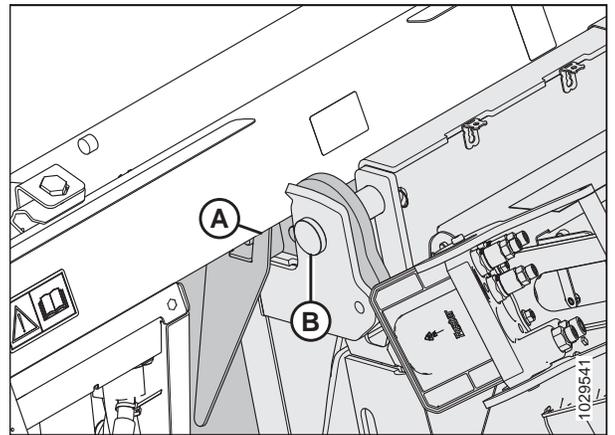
La poutre supérieure reposant sur le convoyeur
